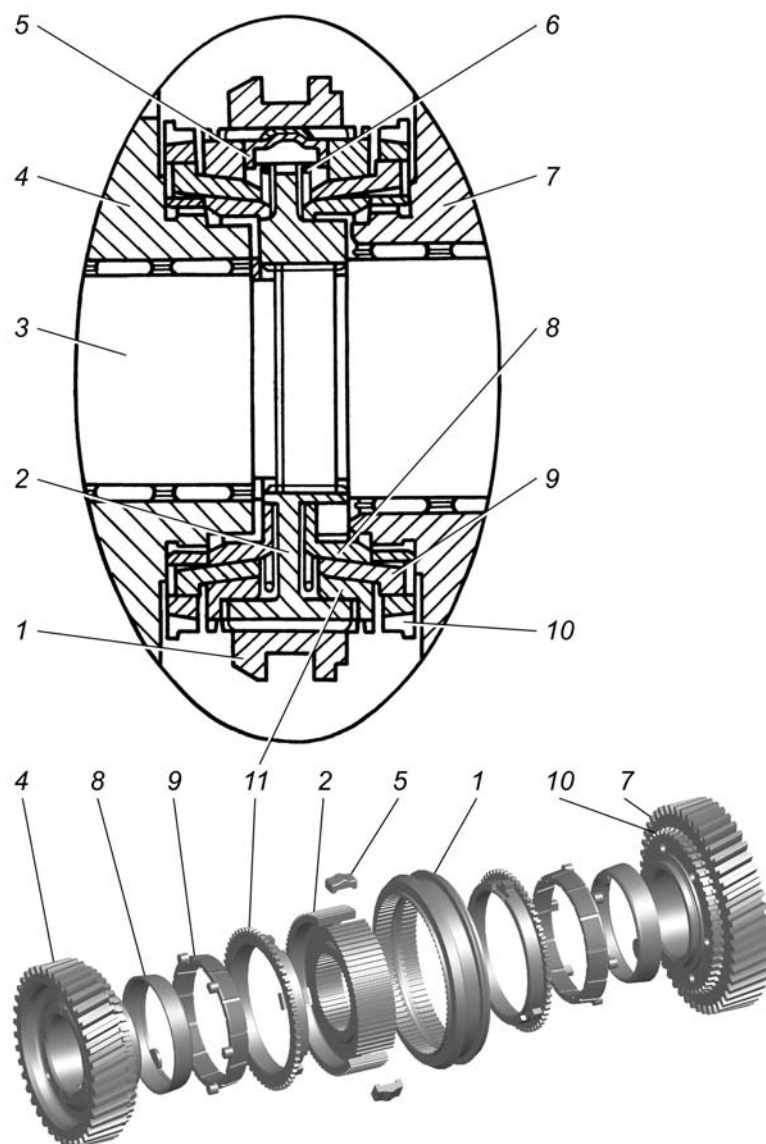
Двухконусный синхронизатор 1-й – 2-й передач: 1 – муфта; 2 – ступица; 3 – вторичный вал; 4 – шестерня 2-й передачи; 5 – сухарь синхронизатора; 6 – пружина синхронизатора; 7 – шестерня 1-й передачи; 8 – кольцо внутреннее; 9 – кольцо среднее; 10 – зубчатый венец; 11 – кольцо наружное
